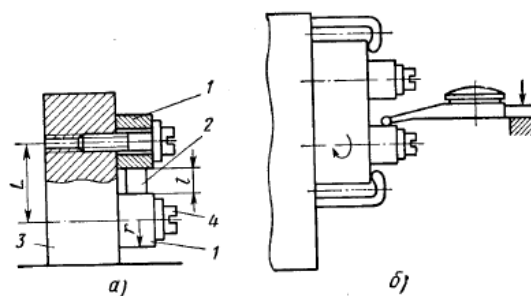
Схема установки еталонних втулок і вивіряння положення деталі по індикатору
